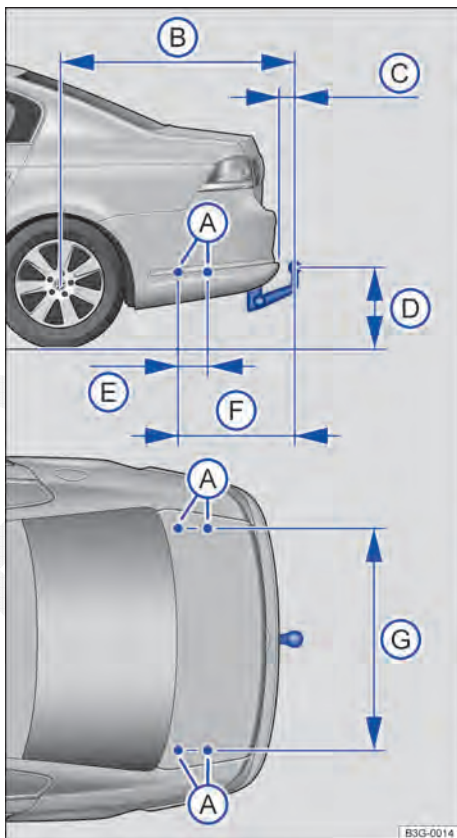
Dimensões e pontos de fixação para instalação posterior de um dispositivo de reboque (Passat).
